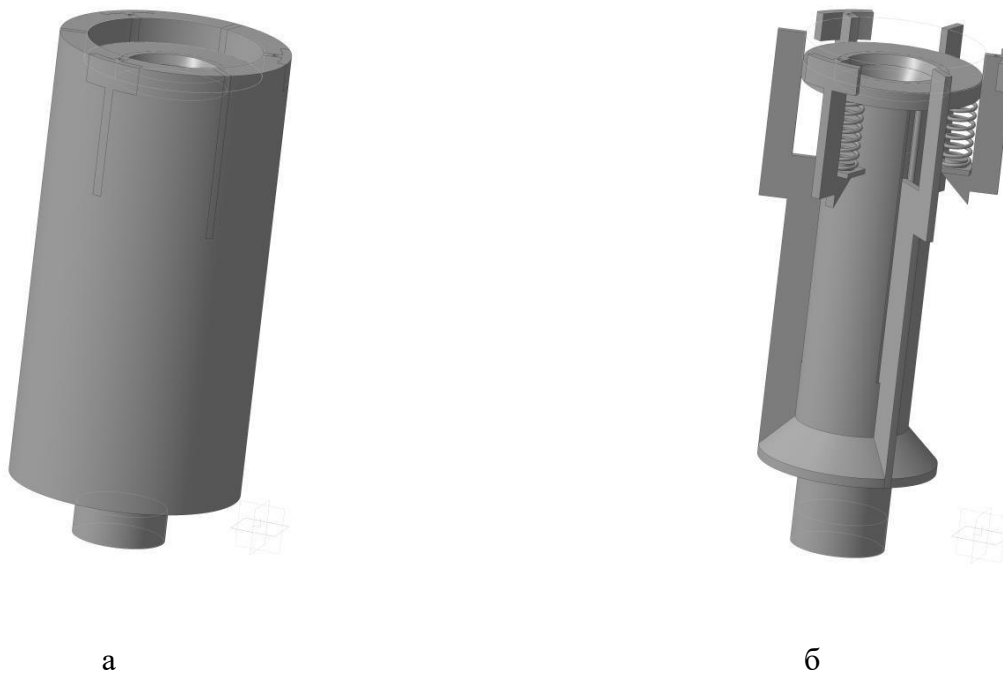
Трехмерная модель шаропитателя а – в корпусе; б – без корпуса
